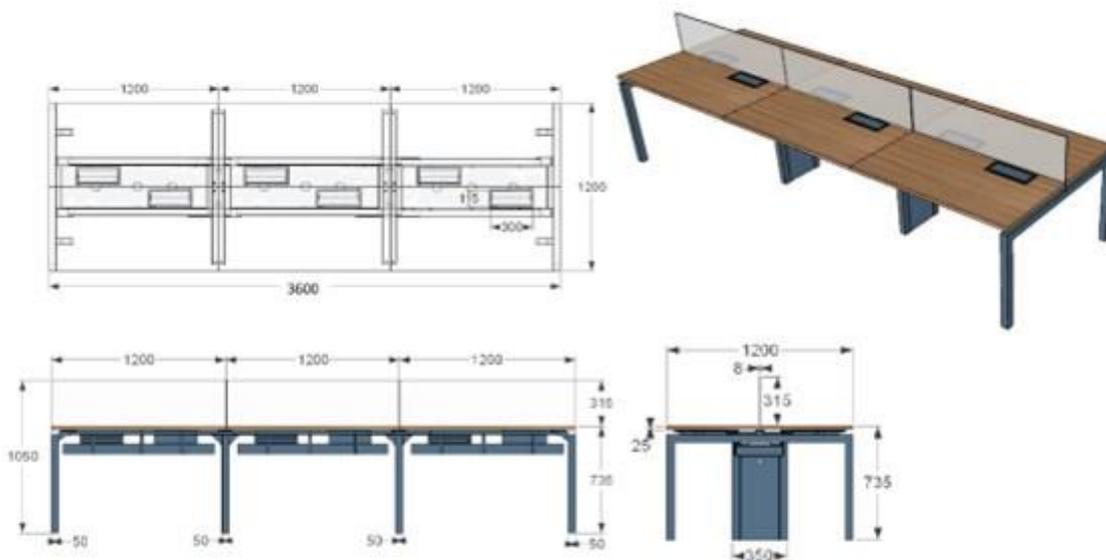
Planta baixa, vista frontal, vista lateral e perspectiva modelo item 18
